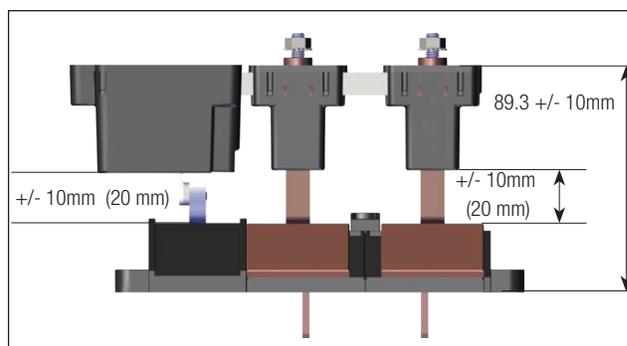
Dimensions hors tout et Dimension de mouvement de brosse admissible
